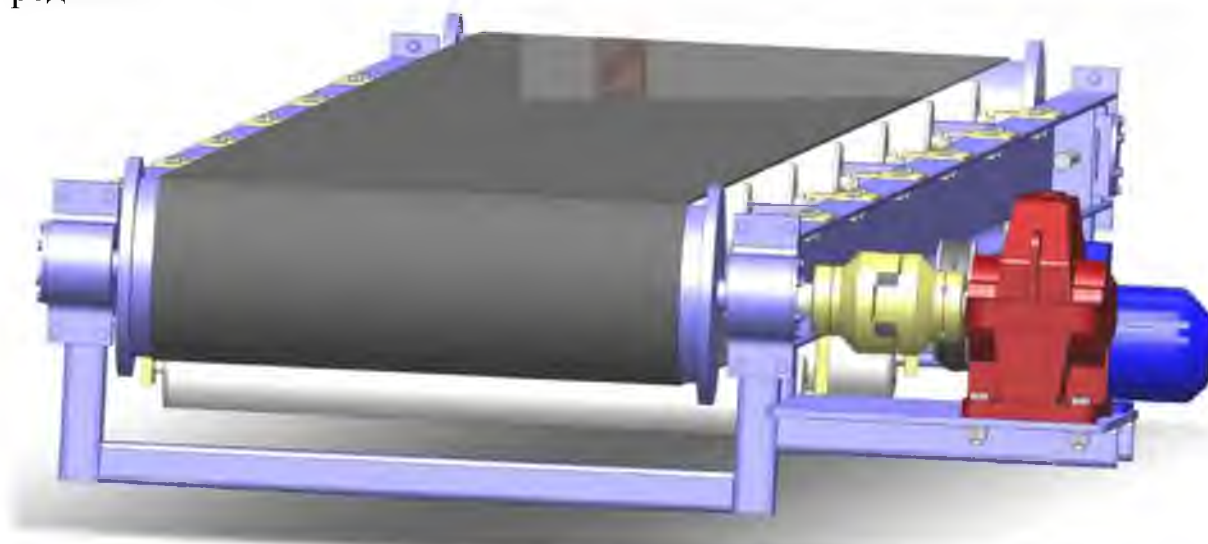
Редукторный привод ленточного транспортера со специальной соединительной муфтой
